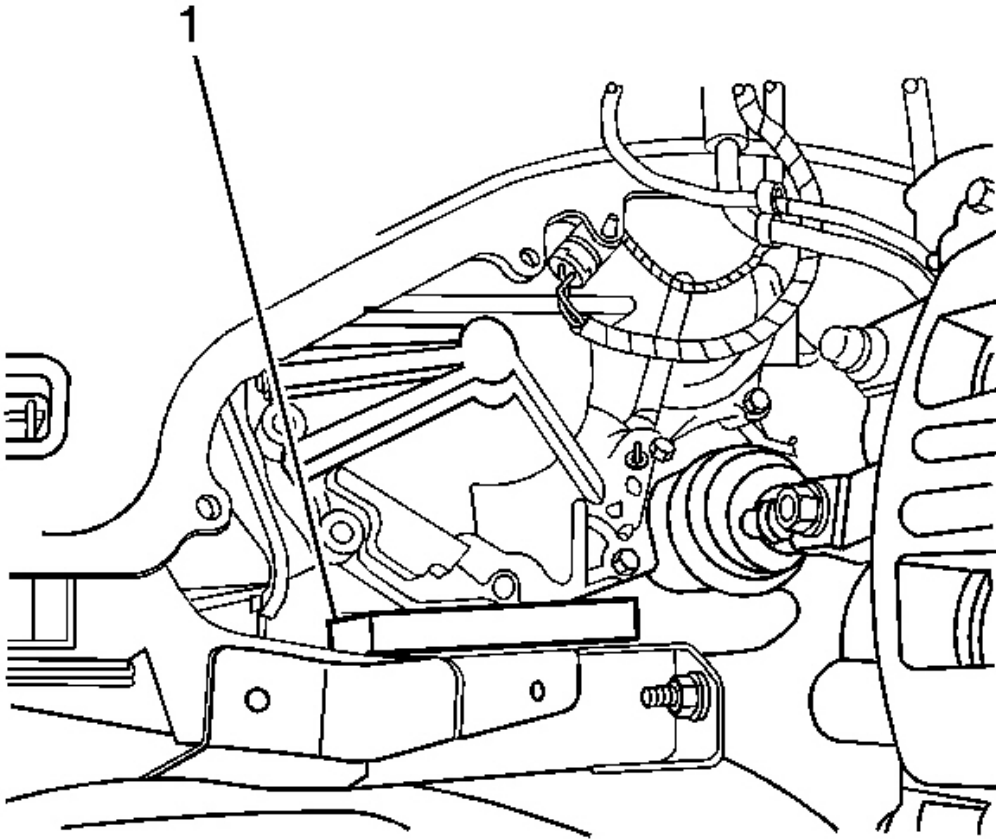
Vista de la derecha Motor Mount & Bolts
